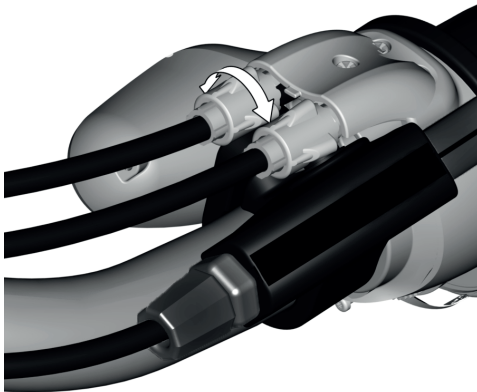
Reduzierung oder Erhöhung des Kabelspiels durch Drehen der Zugeinstellschraube am Griffschalter
